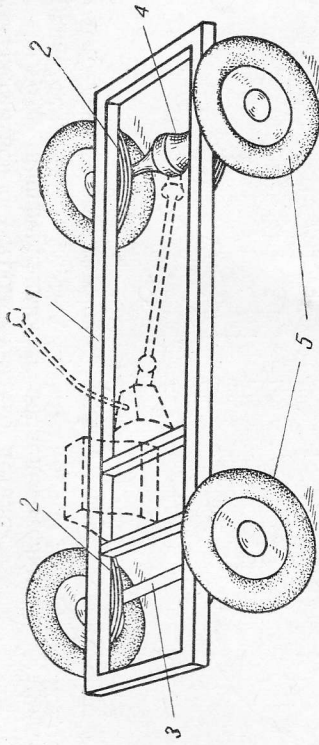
Схема расположения на автомобиле деталей ходовой части:
